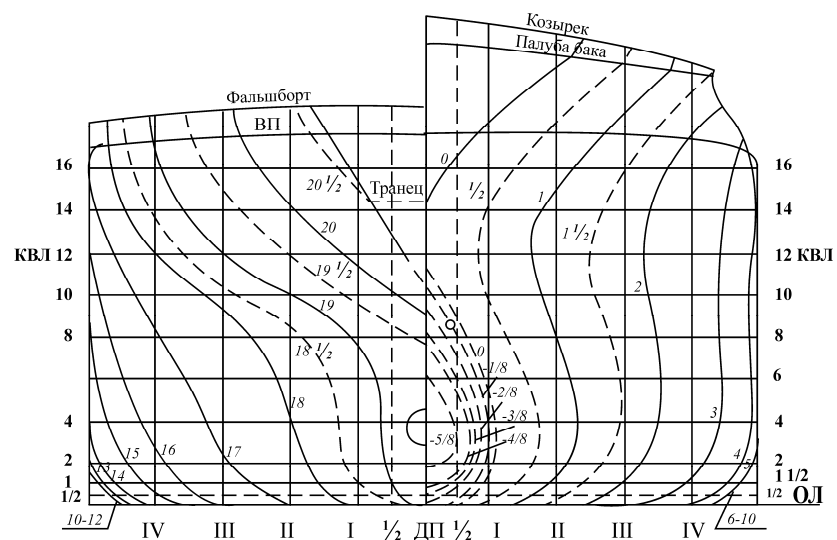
в. Теоретический чертеж транспортного рефрижератора (вариант С), проекция корпус.
